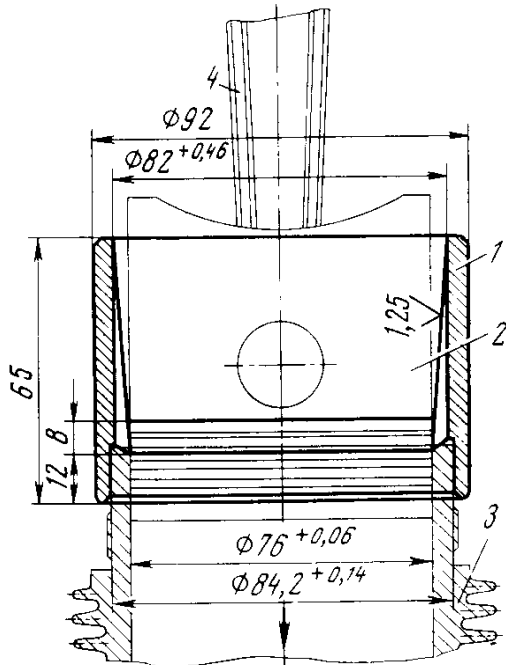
Оправка для установки поршня с кольцами в цилиндр: 1—оправка; 2—поршень в сборе с кольцами и шатуном; 3—цилиндр; 4—шатун
